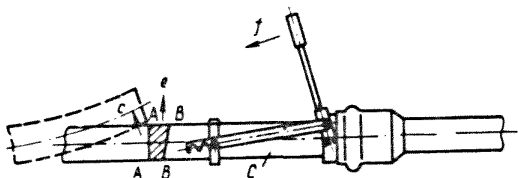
Закрепление рычажного приспособления для демонтажа трубы
